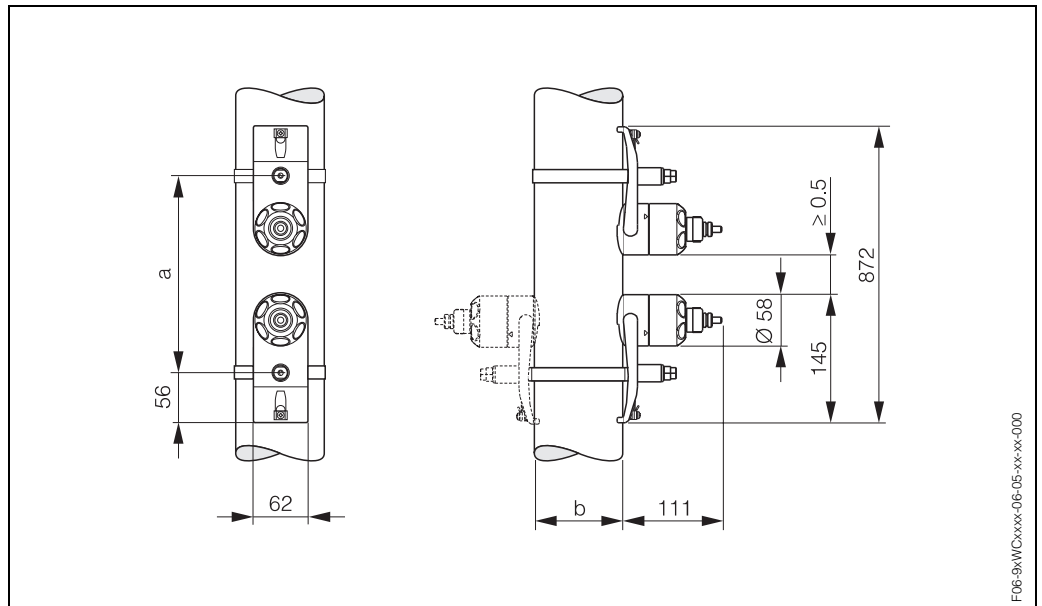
Dimensiones de los sensores W (versión clamp on)
